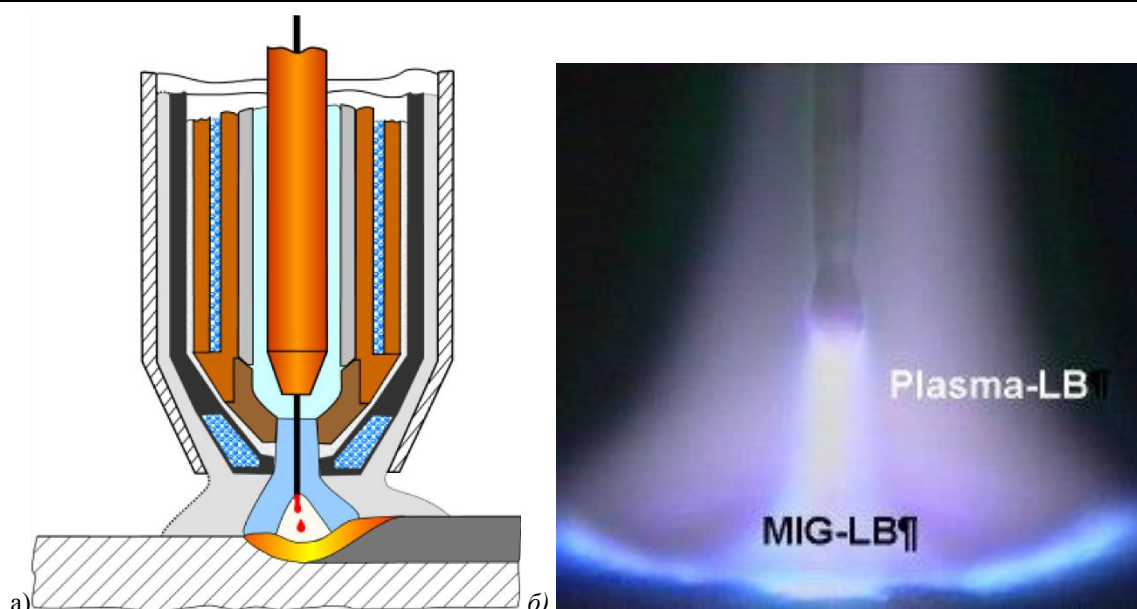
Схема процесса (а) и фотография совместного действия сжатой дуги и дуги плавящегося электрода (б) гибридной плазменно-дуговой сварки.
